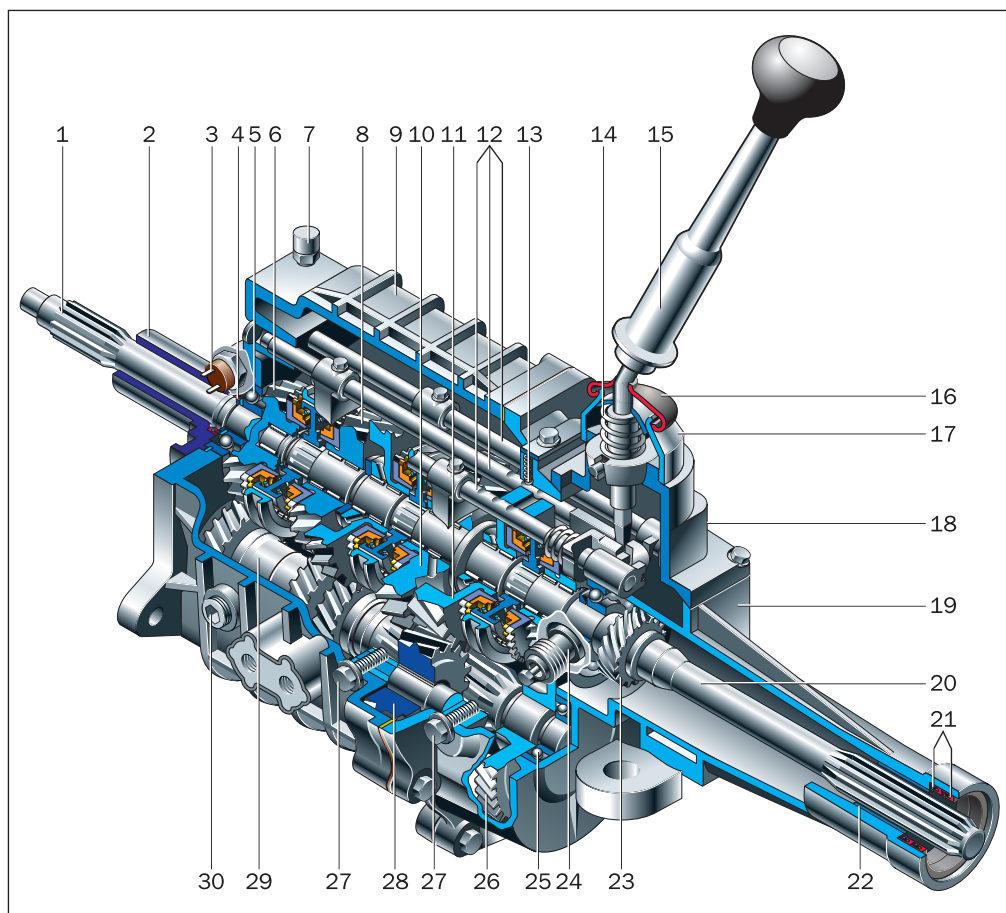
Трехвальная коробка передач: 1 — первичный вал; 2 — крышка подшипника; 3 — выключатель света заднего хода; 4 — манжета первичного вала; 5 — задний подшипник первичного вала; 6 — шестерня привода промежуточного вала; 7 — сапун; 8 — шестерня III передачи; 9 — передний картер; 10 — шестерня I передачи; 11 — шестерня заднего хода; 12 — штоки переключения передач; 13 — шарик-фиксатор; 14 — пружина; 15 — рычаг переключения; 16 — защитный уплотнитель; 17 — колпак рычага; 18 — корпус рычага переключения; 19 — задний картер; 20 — вторичный вал; 21 — манжеты удлинителя заднего картера; 22 — сталебабитовая втулка; 23 — шестерня привода спидометра; 24 — привод спидометра; 25 — задний подшипник промежуточного вала; 26 — шестерня V передачи; 27 — болты крепления оси промежуточной шестерни заднего хода; 28 — промежуточная шестерня заднего хода; 29 — промежуточный вал; 30 — маслозаливная пробка
